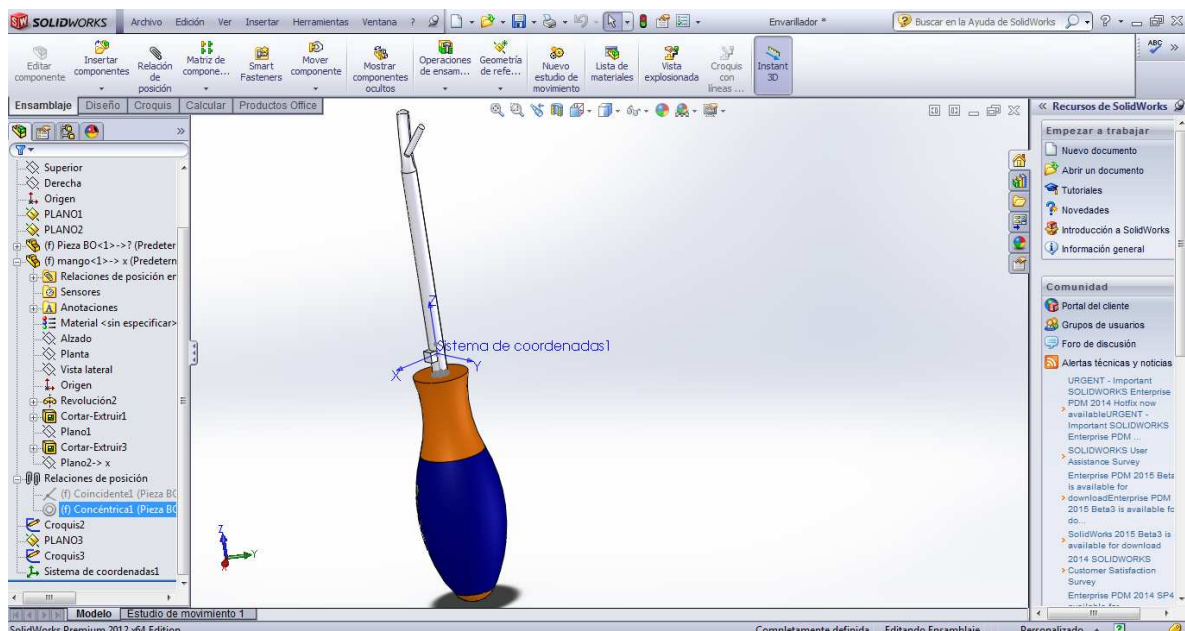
Vista 2 del conjunto completo (herramienta+acelerómetro) en SOLIDWORKS
